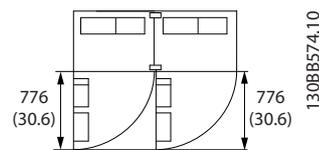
Пространство перед корпусом IP21/IP54, типоразмер F10
